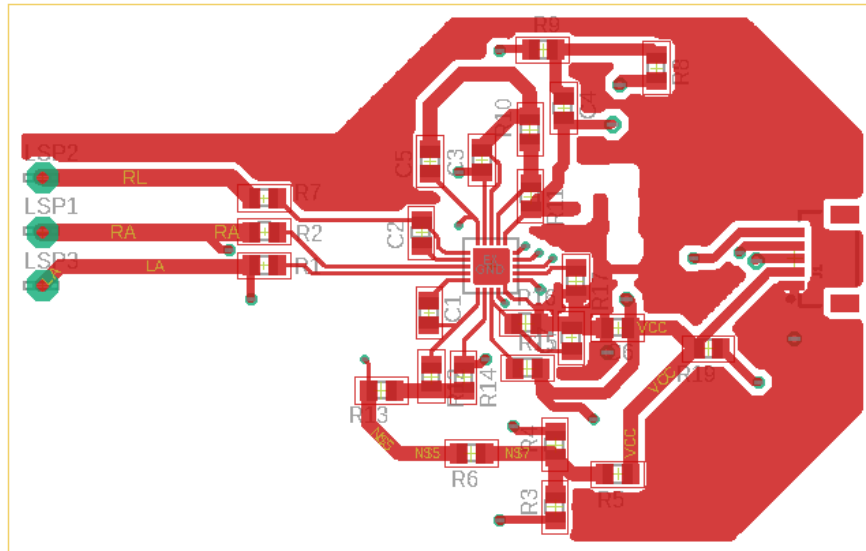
Vista de la superficie de la tarjeta PCB del bloque ECG
